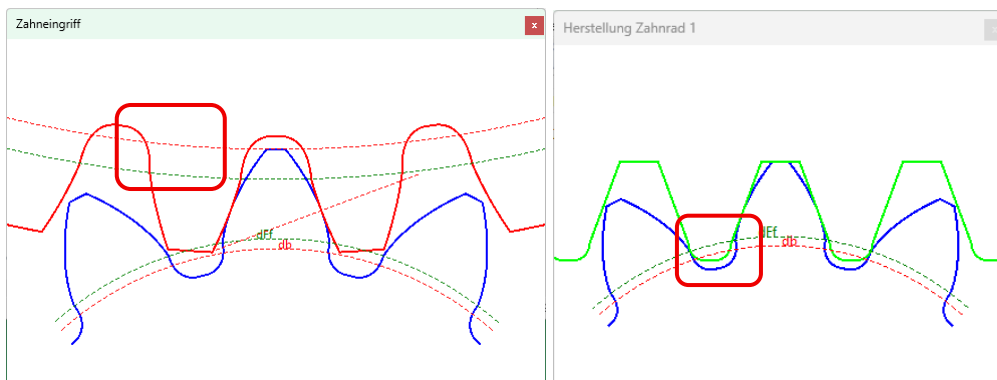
Links: Eingriff, Zahnräder mit Unterschnitt. Rechts: Eingriff Bezugsprofil Werkzeug zu Zahnrad, Werkzeug mit Protuberanz.
